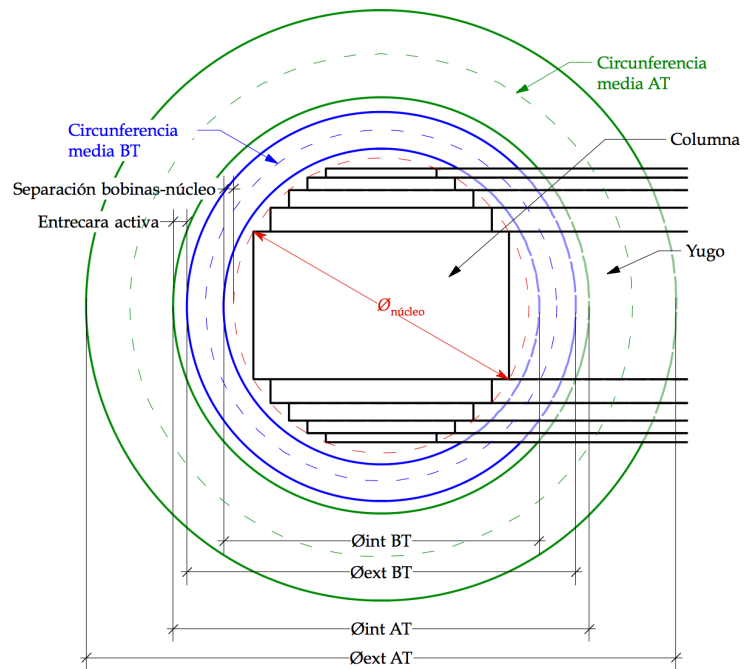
Dimensiones del bobinado concéntrico (BT interior, AT exterior)
